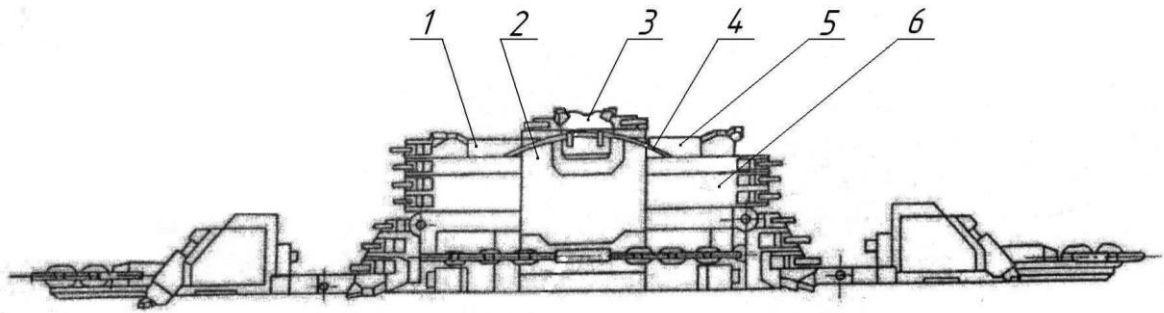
Исполнительный орган с рессорной регулировкой высоты
